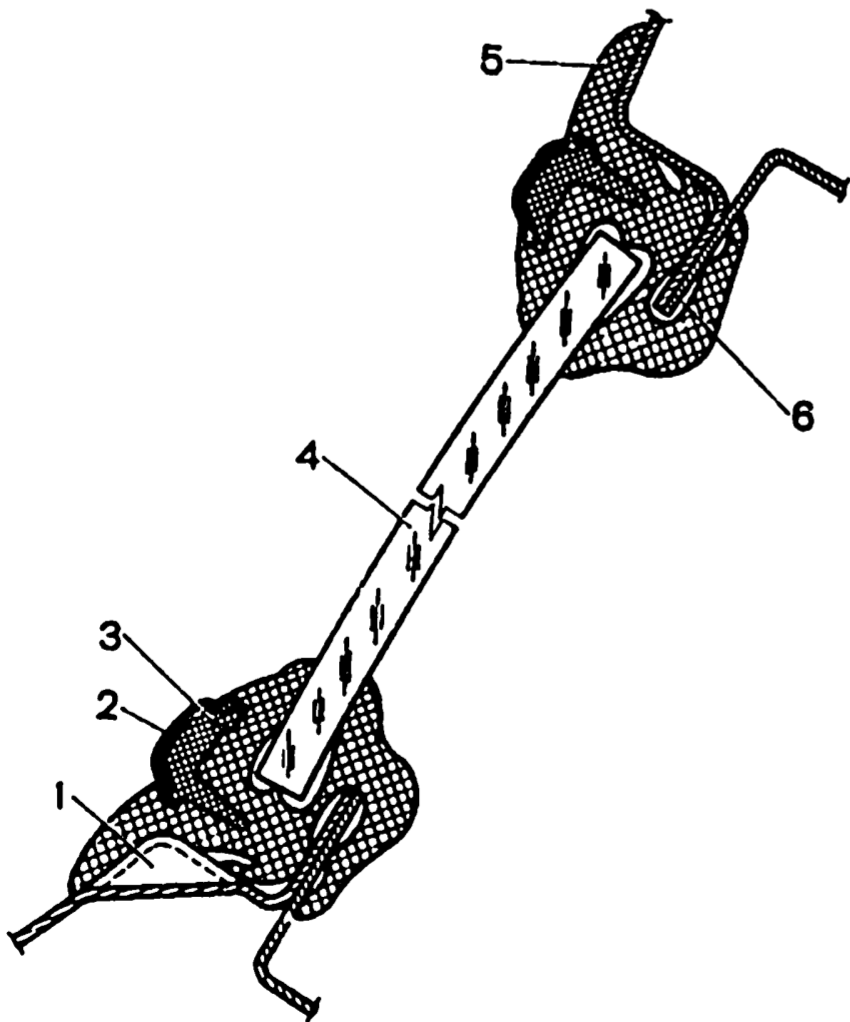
Ветровое стекло с уплотнителем в сборе: 1 - штамповка для стока воды; 2 - облицовка окантовки уплотнителя; 3 - окантовка уплотнителя; 4 - стекло; 5 - уплотнитель; 6 - фланец проема ветрового окна
